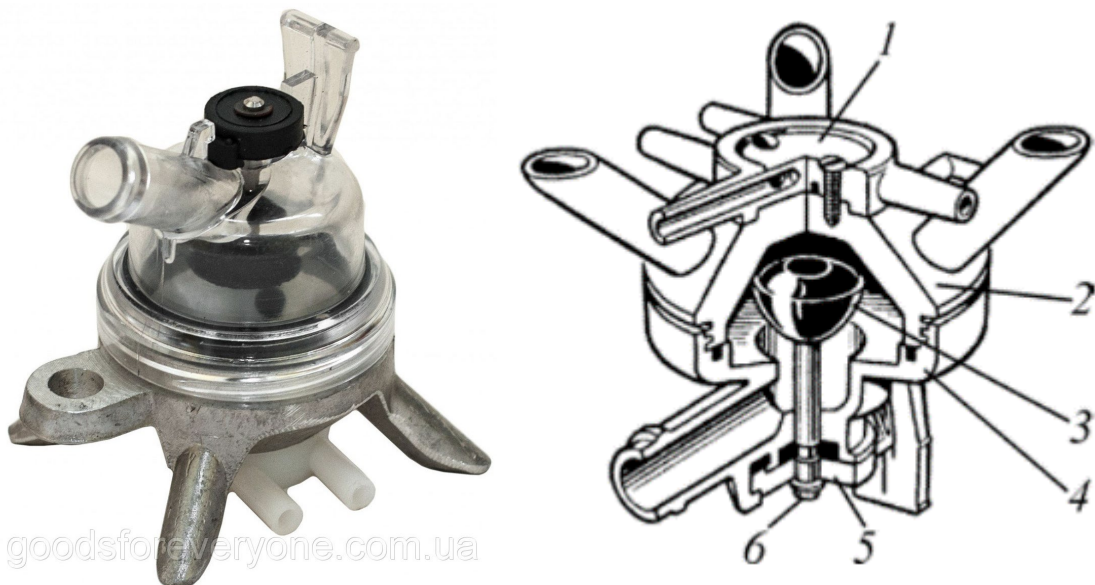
Колектор АДУ-1: 1 - розподільник; 2 – верхній корпус; 3 – клапан; 4 – нижній корпус; 5 - шайба; 6 – шплінт
